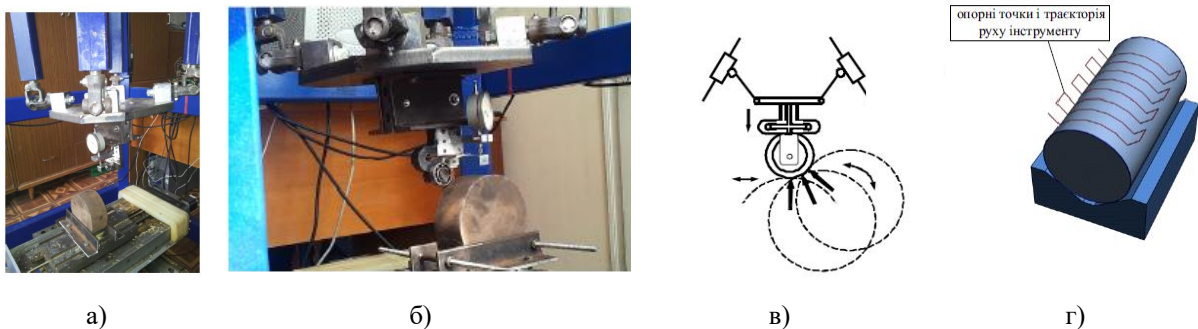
Загальний вигляд верстату з МПС і жорстке кріплення оброблюваного циліндру
